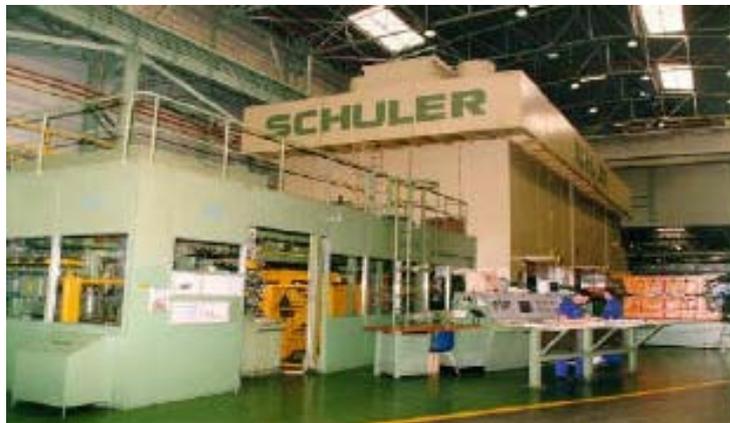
Prensa Triaxial de la Planta de Prensas
